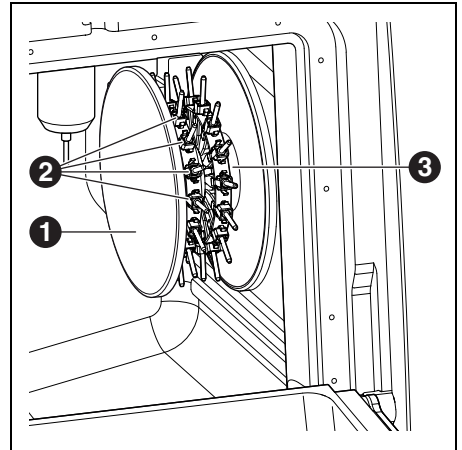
Vista general del depósito de herramientas (Tool Blank) en posición retraída
